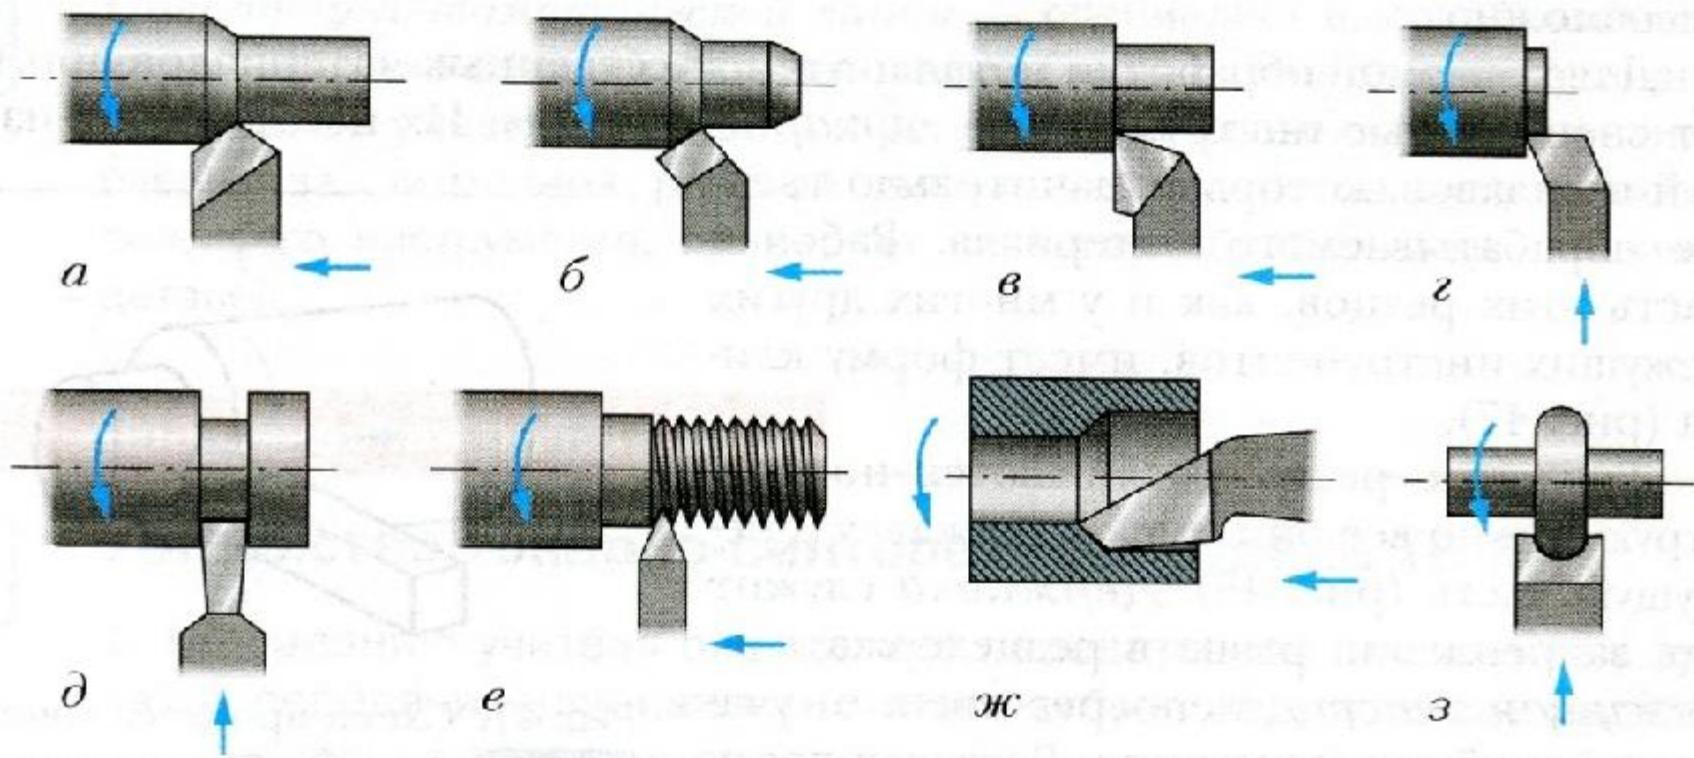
Токарные резцы: *а* — проходной прямой; *б* — проходной отогнутый; *в* — проходной упорный; *г* — подрезной; *д* — отрезной; *е* — резьбовой; *ж* — проходной расточкой; *з* — фасонный
